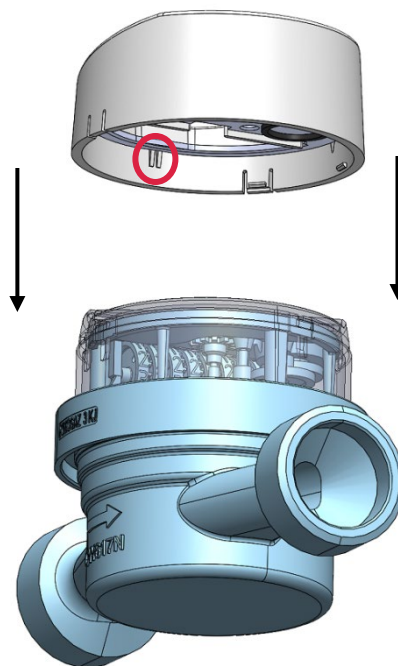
Ansicht des Wasserzähleraufsatzes OP-O4-1a, vor der Montage auf dem Wasserzähler.
